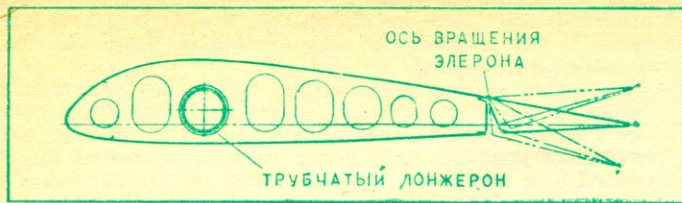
Схема подвески элерона на крыле планера АНБ.
